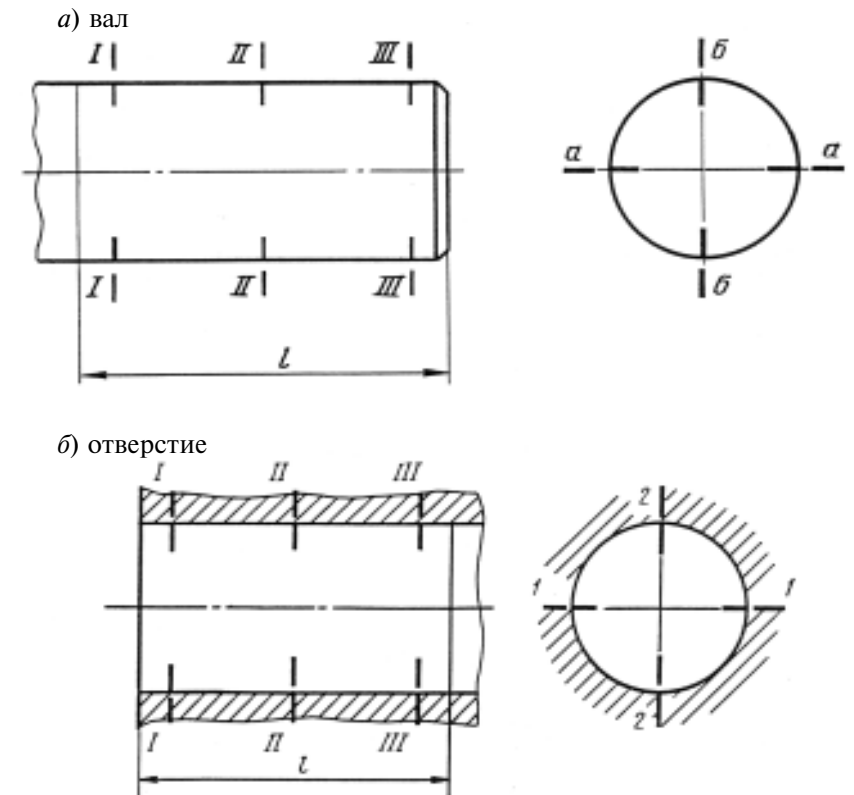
Схема измерения деталей гладкого цилиндрического соединения
